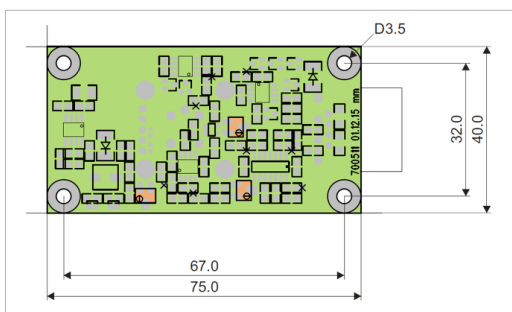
FCX-MP1000-Extern-CH PCB 电子布局图 (板背面)
